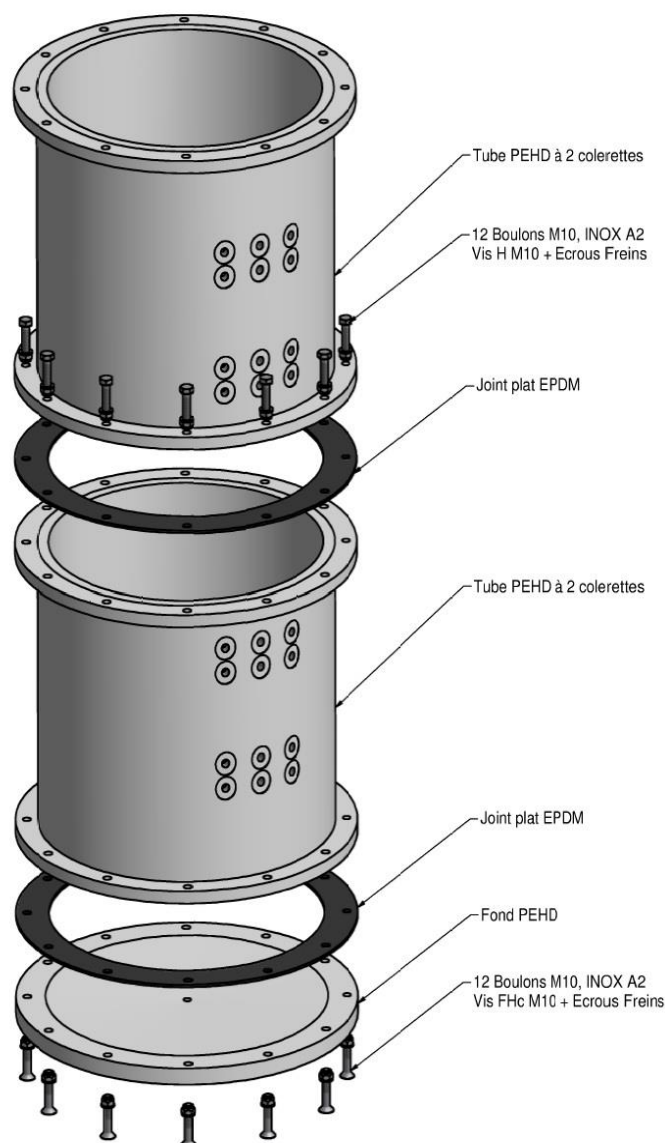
Vue éclatée de la colonne utilisée couramment à l'Ecotron. Chaque section de tube en PEHD fait 36 cm de haut pour 36,5 cm de diamètre interne et est équipée de brides de serrage en PEHD. Chaque section possède latéralement 12 trous de dimension 12 mm pour permettre l'insertion de capteurs. Les sections peuvent être fixées entre elles de façon étanche grâce à des joints plats en EPDM serrés dans des brides par 12 boulons.
